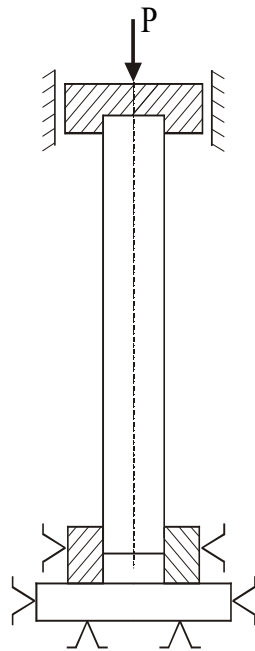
Способ установки и закрепления деталей при запрессовке (свободный конец вала допускает угловые повороты): 1 – стол; 2 – втулка; 3 – вал; 4 – пуансон прессы; 5 – закрепительная втулка
